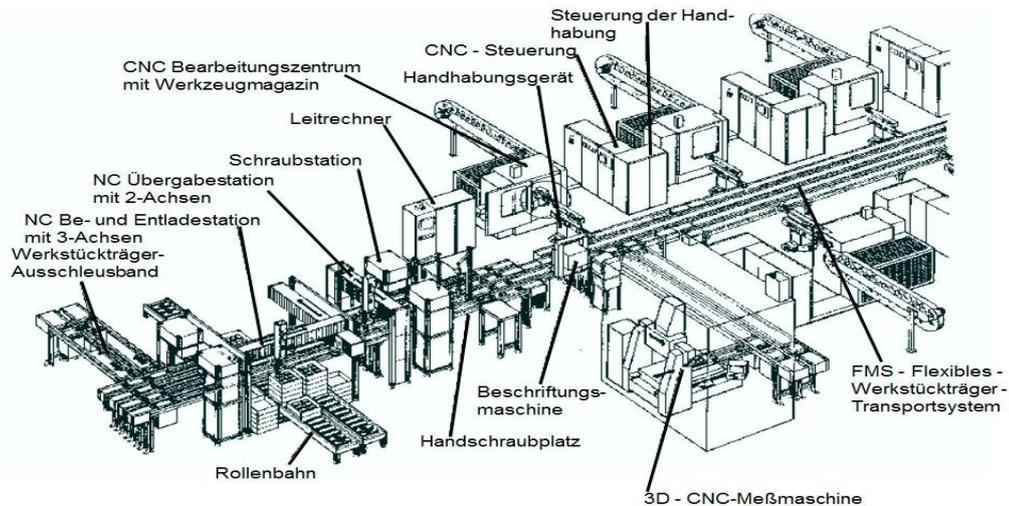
Elemente und Grundaufbau eines FFS (BOSCH Industrieausrüstung, Anwender BOSCH Stuttgart)(1)
